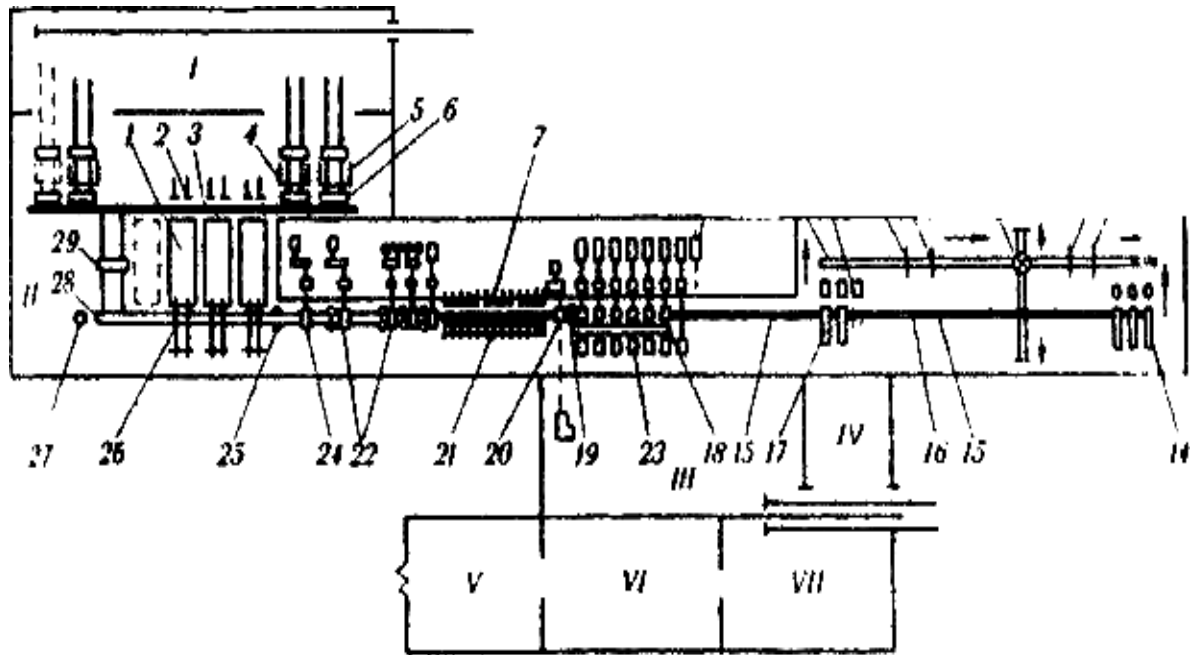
Схема розташування встаткування стану 2000 Череповецького металургійного комбінату:
